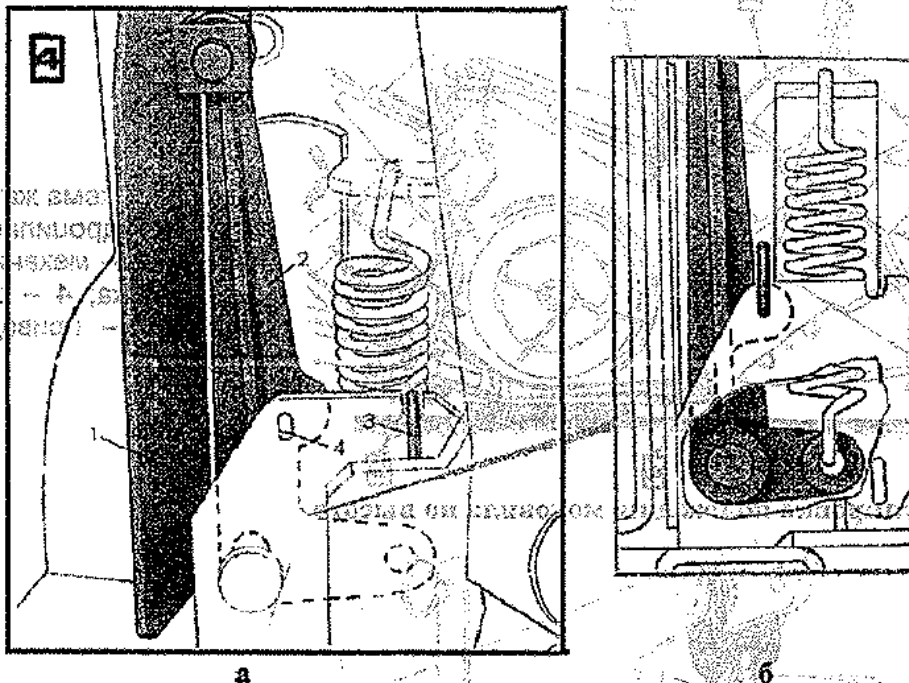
Схема боковых щитков: а-щиток прижат; б-щиток отведен; 1-щиток; 2-рычаг; 3-шплинт; 4-отверстие
